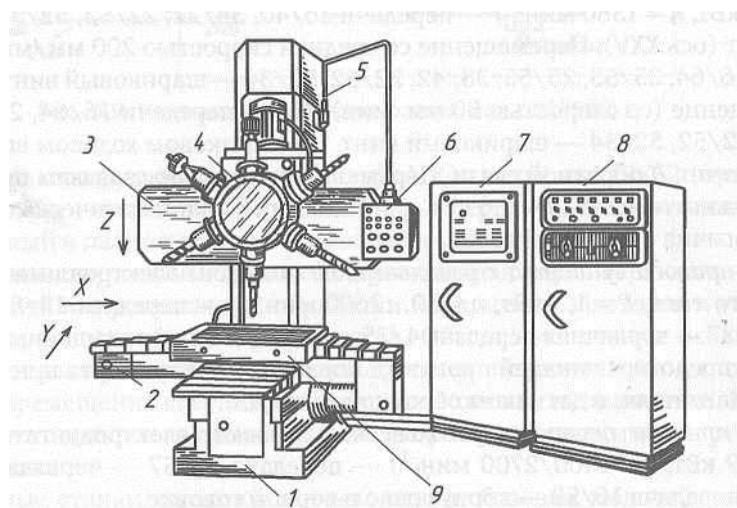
Общий вид вертикально-сверлильного станка мод. 2Р135Ф2-1
